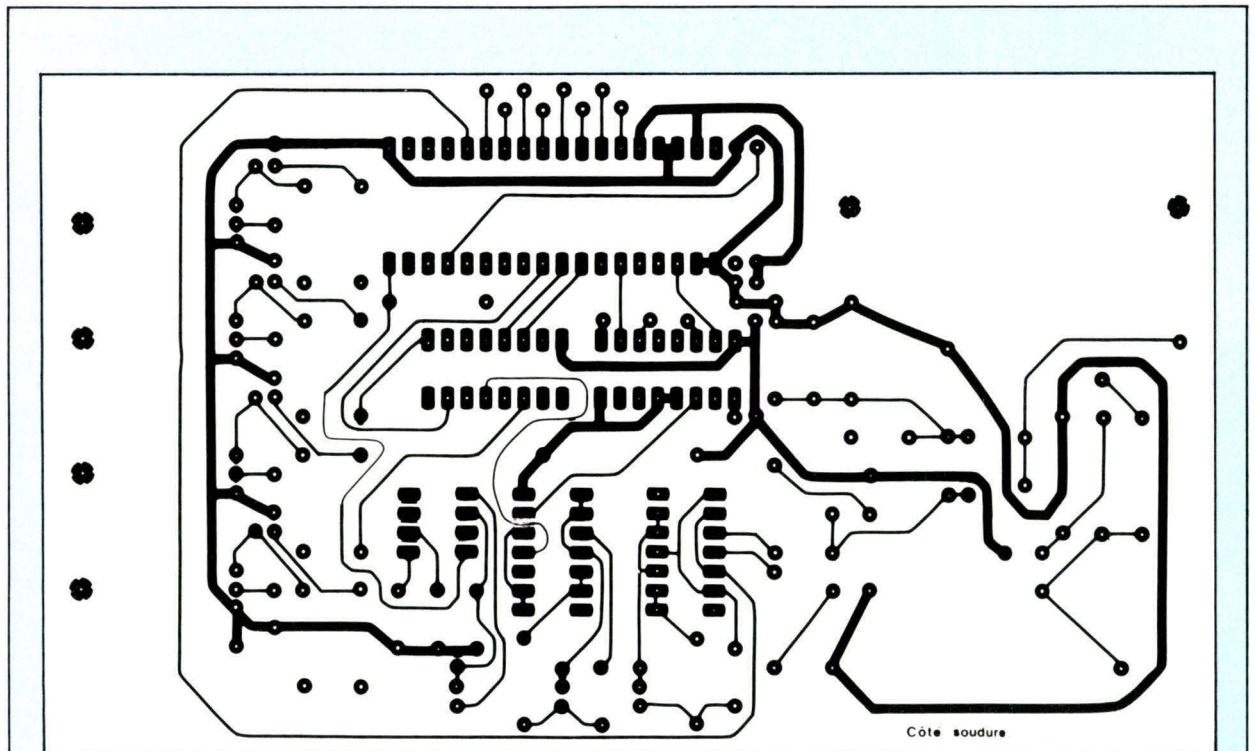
Circuit imprimé d'une carte périphérique vu côté « soudures ».
